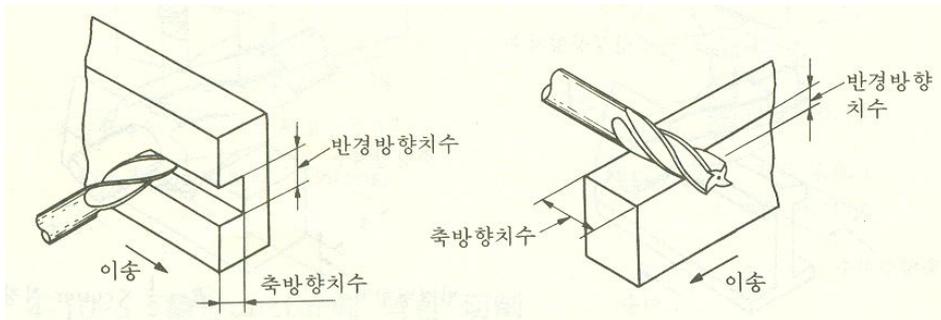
열립 홈절삭(수평 milling machine, 좌)과 원주절삭(수평 milling machine, 우)
